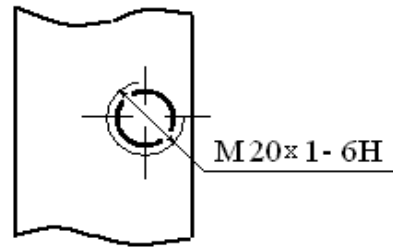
Обозначение внутренней резьбы на чертеже (вид сверху)
